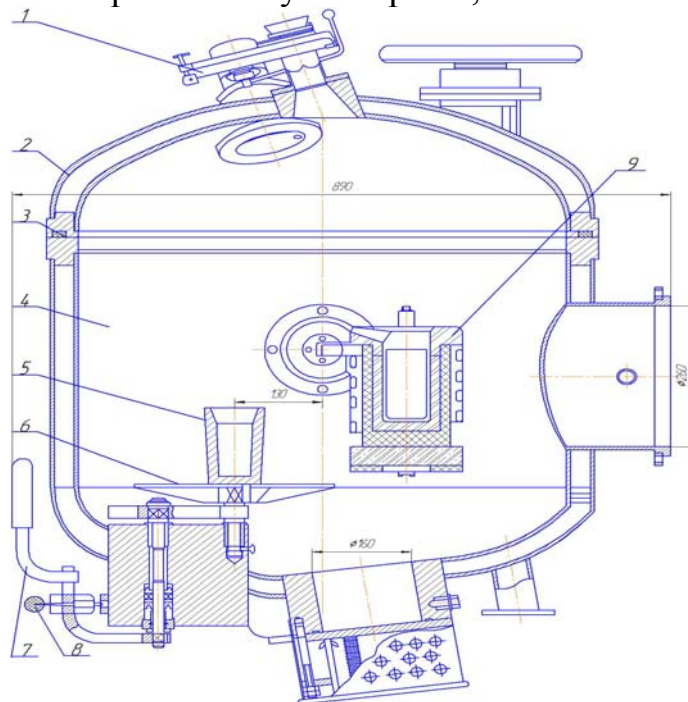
Вакуумная индукционная печь: 1 - система для наблюдения; 2 – верхняя крышка; 3 – прокладка; 4 – камера печи; 5 – изложница; 6 – стол; 7 – рычаг; 8 – фиксатор; 9 – тигель.
